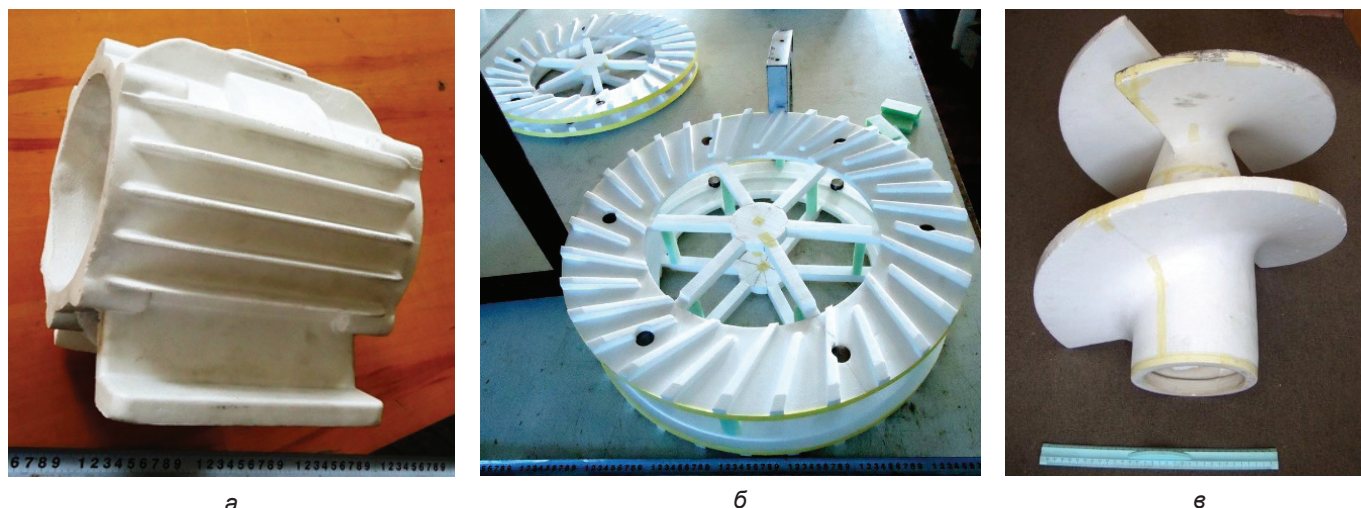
Модели из ППС для получения металлических отливок: корпуса электродвигателя (а); рабочих колес (б); шнека (в)
